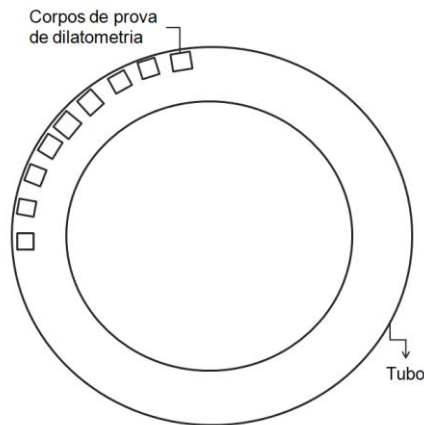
Croqui das posições de retirada dos corpos de prova para dilatométrica.
